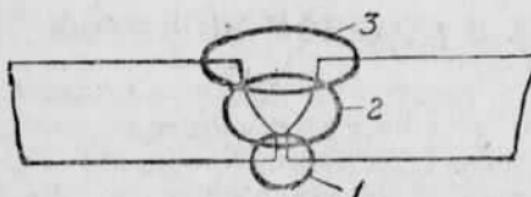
Схема трехслойной сварки продольных швов в трубах большого сечения.
